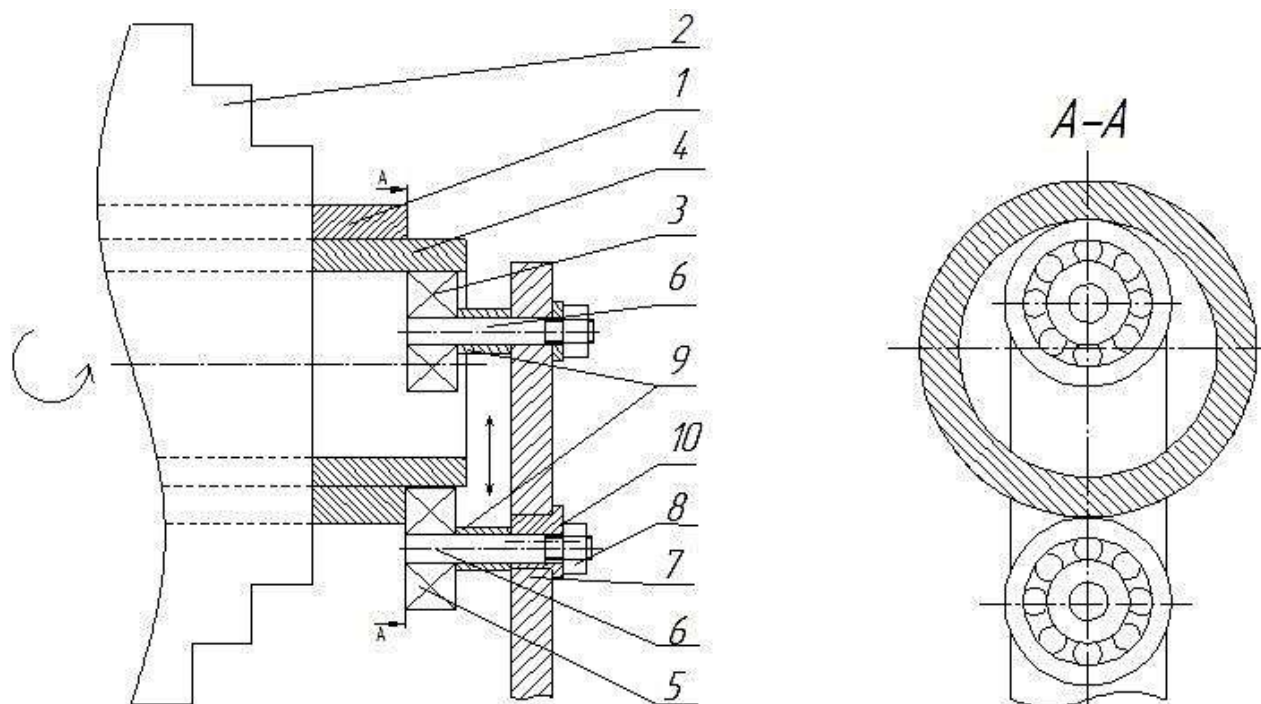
Устройство для отрезки трубчатых заготовок от цилиндрической трубы
